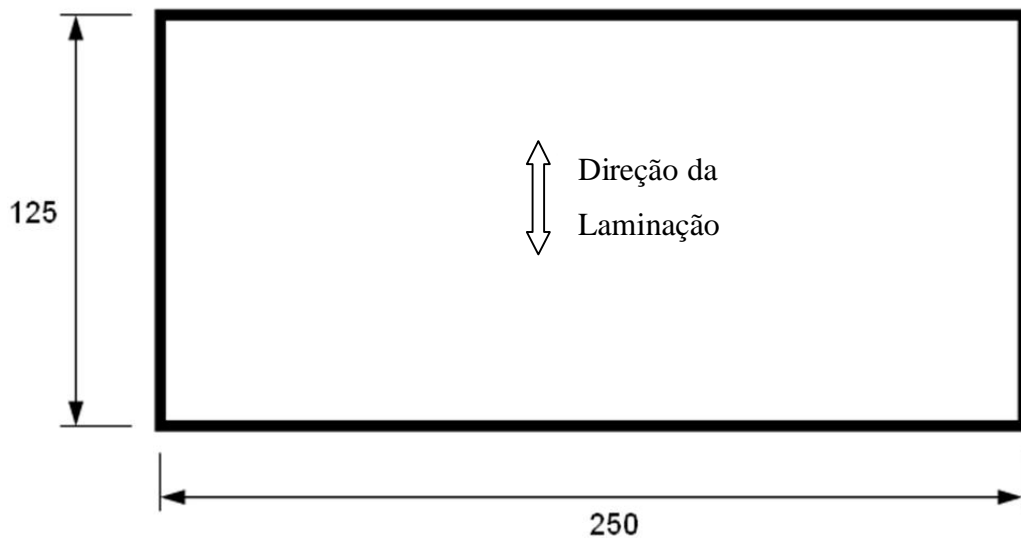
Dimensional da amostra para fabricação das placas soldadas.
